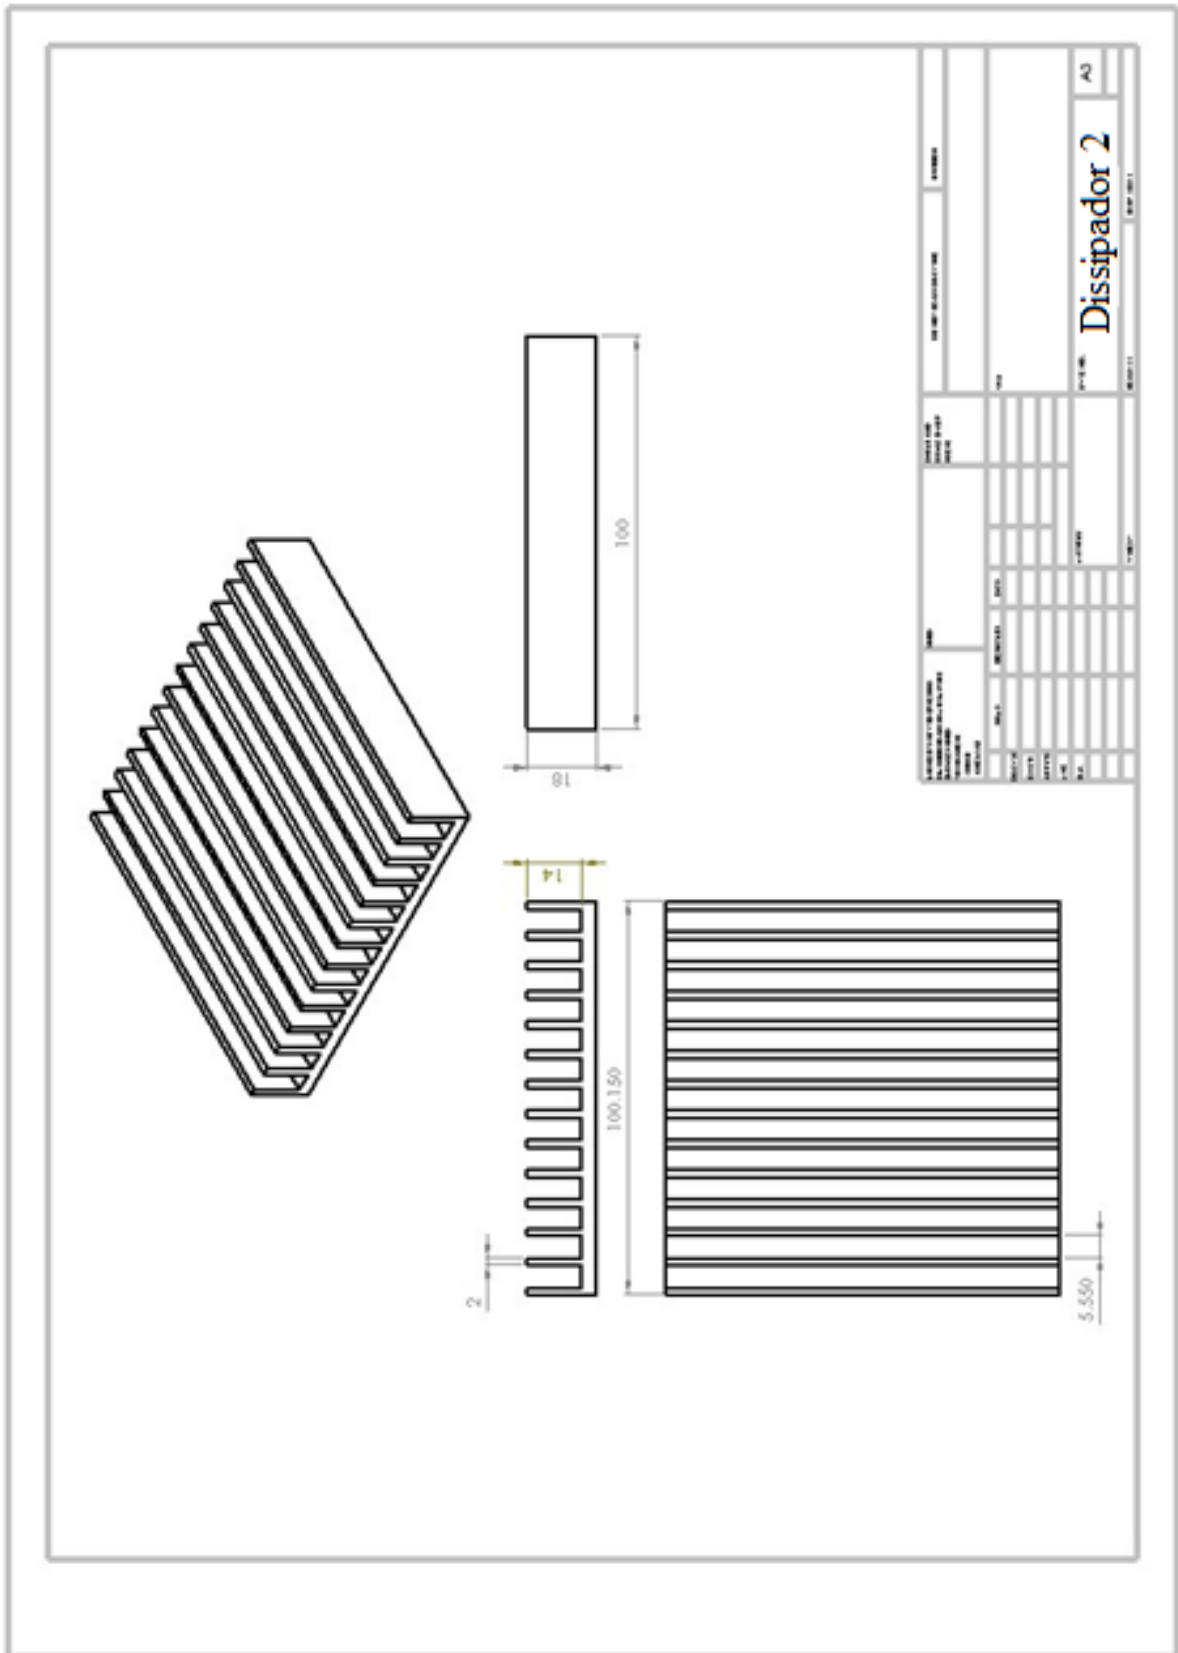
Desenho técnico utilizado para confecção do Dissipador 2.
